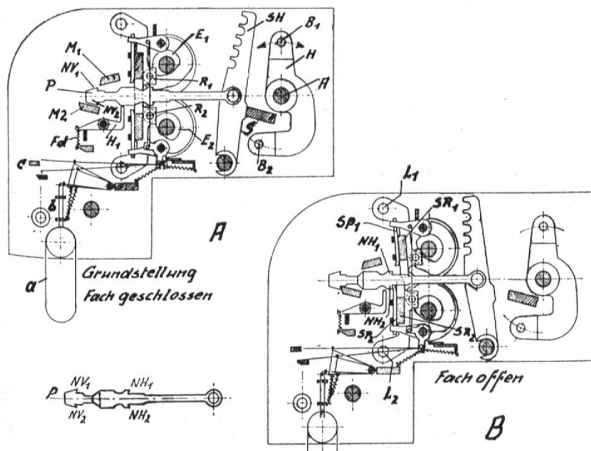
Doppelhub-Offenfach-Schaftmaschine; Platine P mit vier Nasen; Patent Fa. Carl Zangs, Maschinenfabrik, Krefeld; A = Schaft in Grundstellung, B = Schaft gehoben, Fach offen
